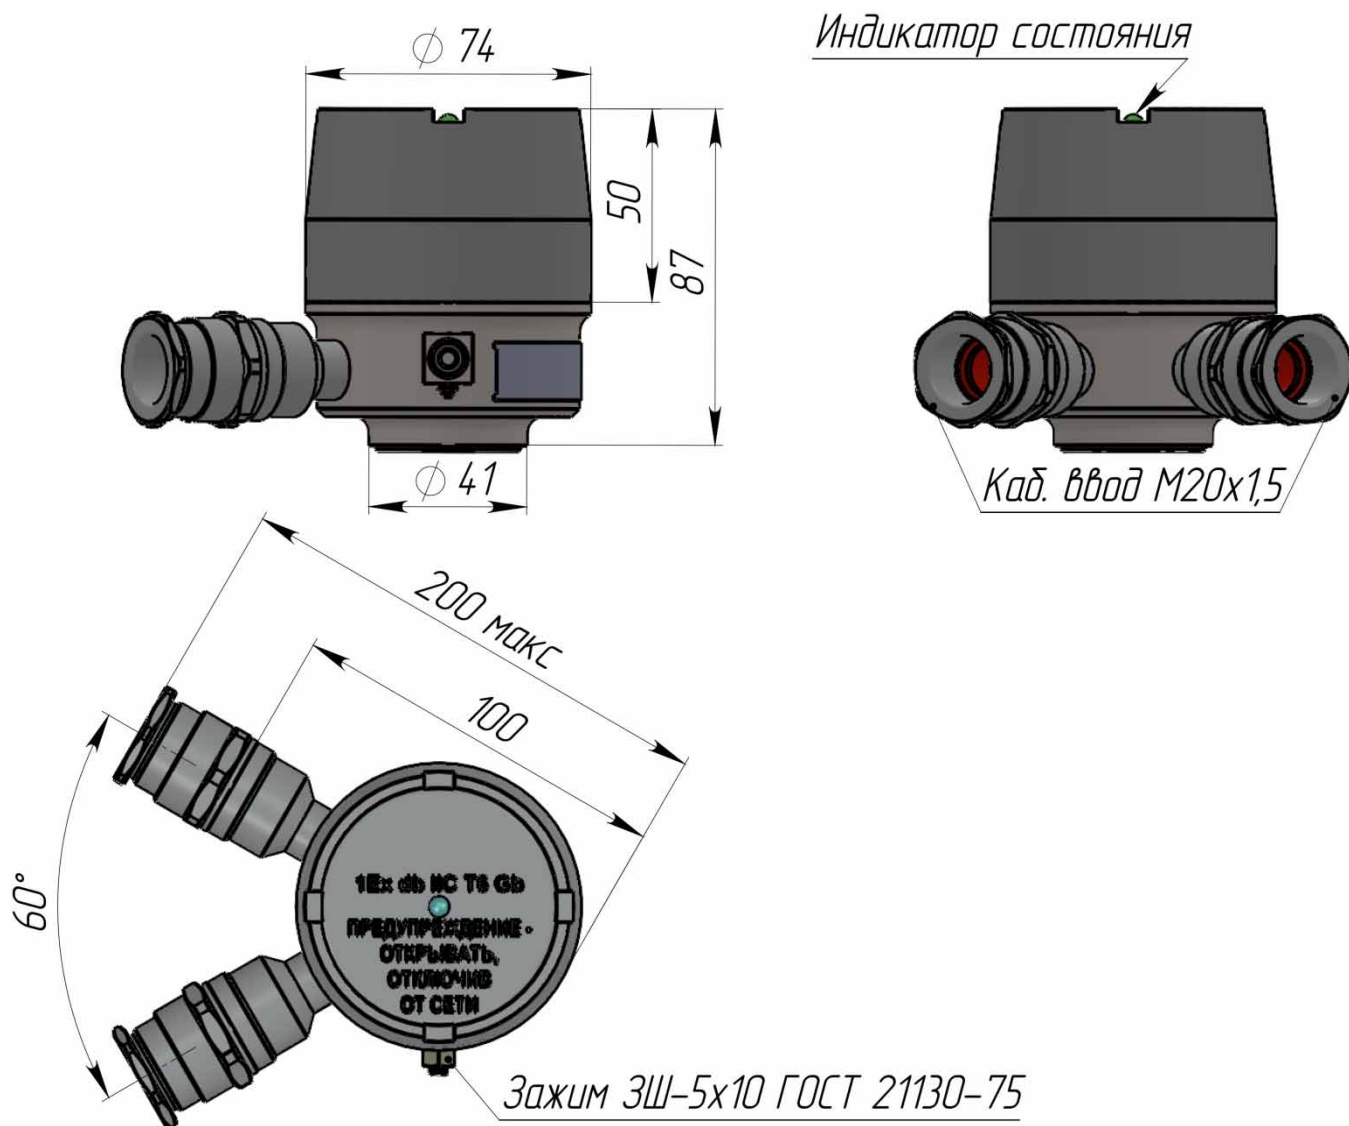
Габаритные размеры корпуса блока электронного в корпусе из нержавеющей стали для оборудования класса безопасности ЗН (высокая крышка, два кабельных ввода)
